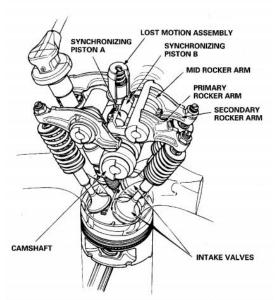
Устройство ГРМ двигателя SOHC, оснащённого системой VTEC (SOHC VTEC): CAMSHAFT — распределительный вал; SYNCHRONIZING PISTON A - синхронизирующий поршень A; LOST MOTION ASSEMBLY — гасящий механизм; SYNCHRONIZING PISTON В — синхронизирующий поршень B; MID ROCKER ARM — центральное коромысло; PRIMARY ROCKER ARM — первичное коромысло; SECONDARY ROCKER ARM — вторичное коромысло; INTAKE VALVES — впускные клапаны
